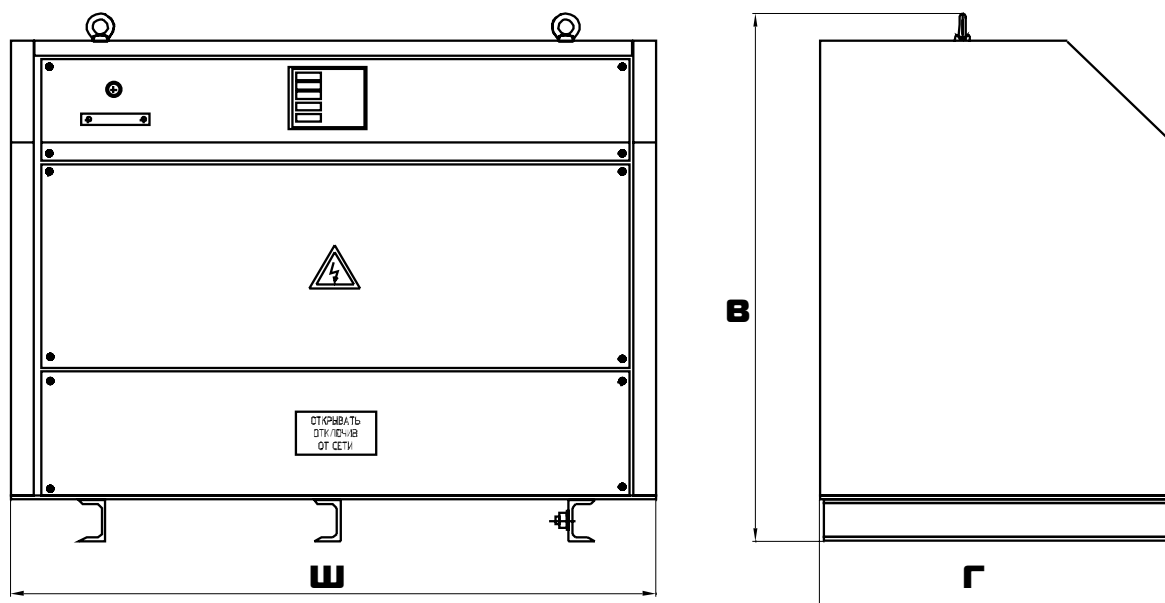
Габаритный чертеж СТС-5-М IP31 (16- 120 кВА)
